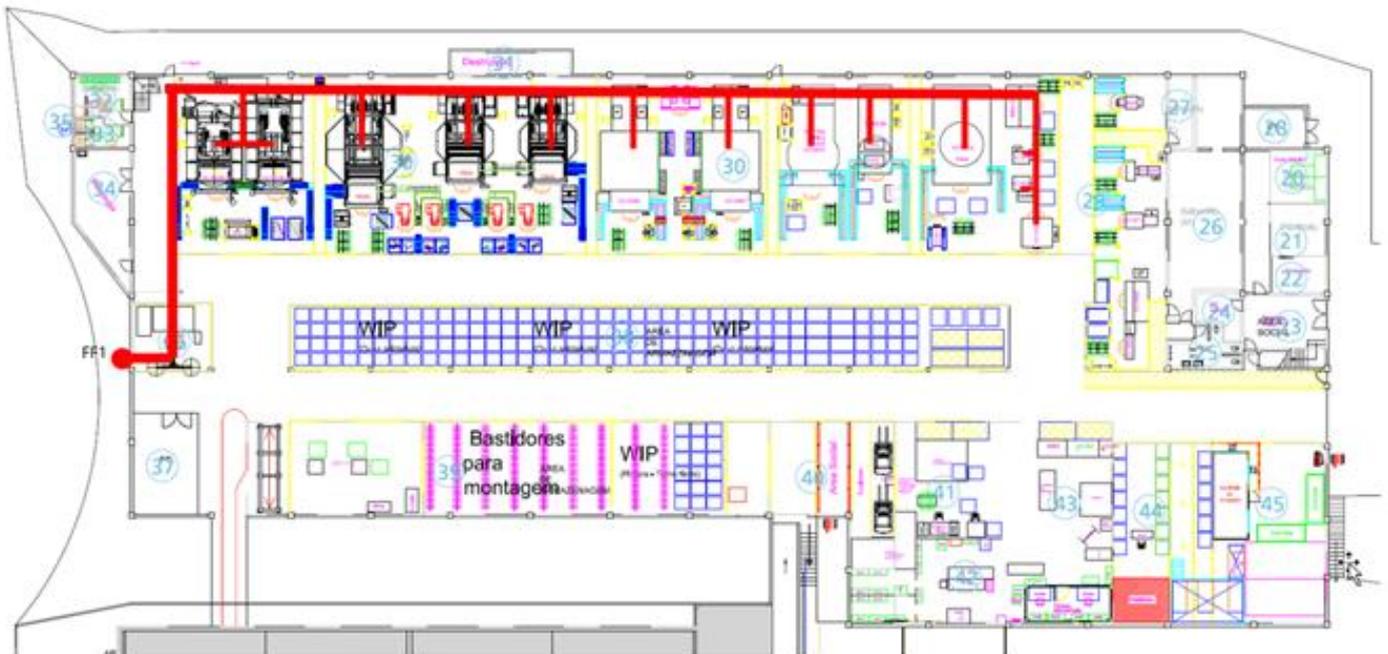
Detalhe do layout da soldadura em vigor em 2014
